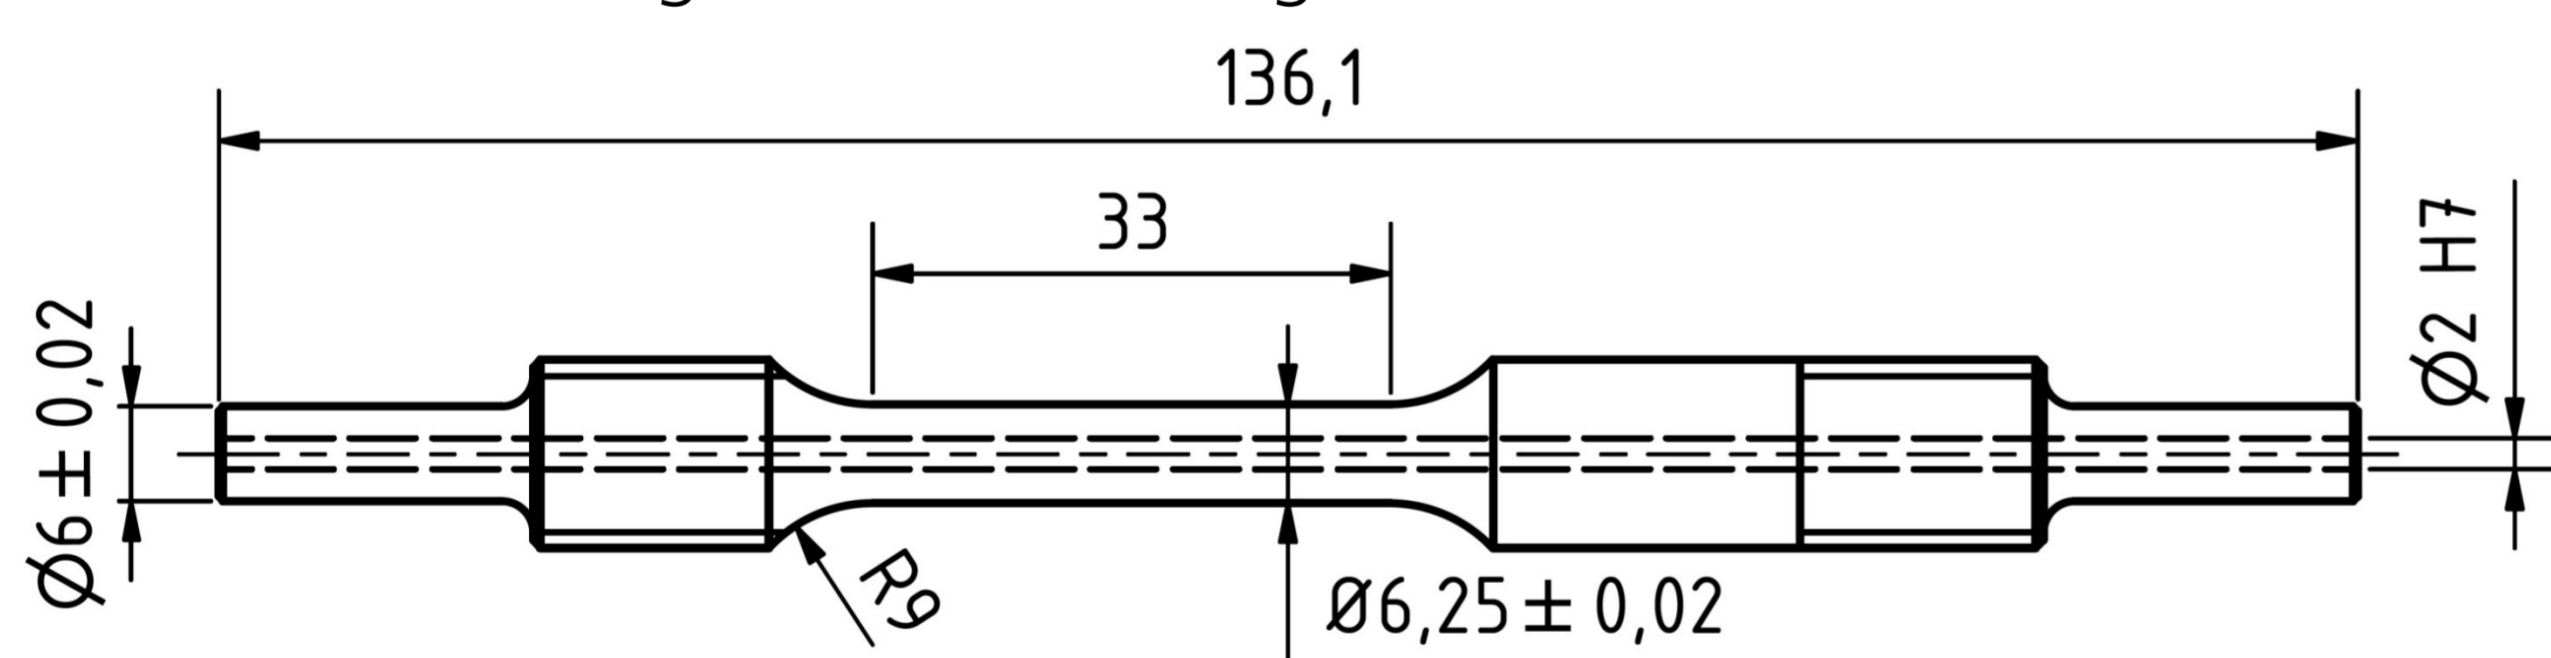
Technische Zeichnung der Hohlprobengeometrie.
